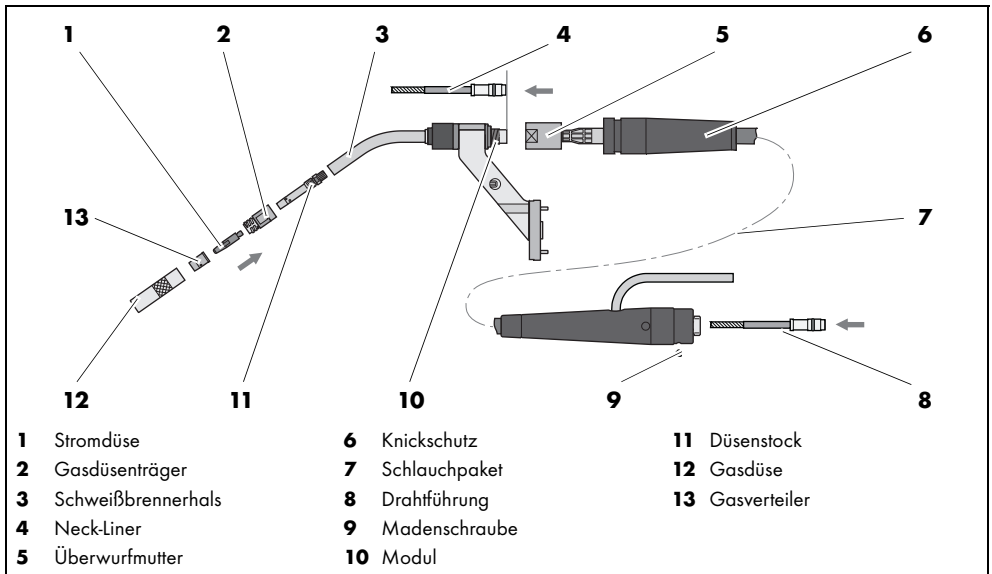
Schweißbrennerhals und Schlauchpaket ausrüsten
